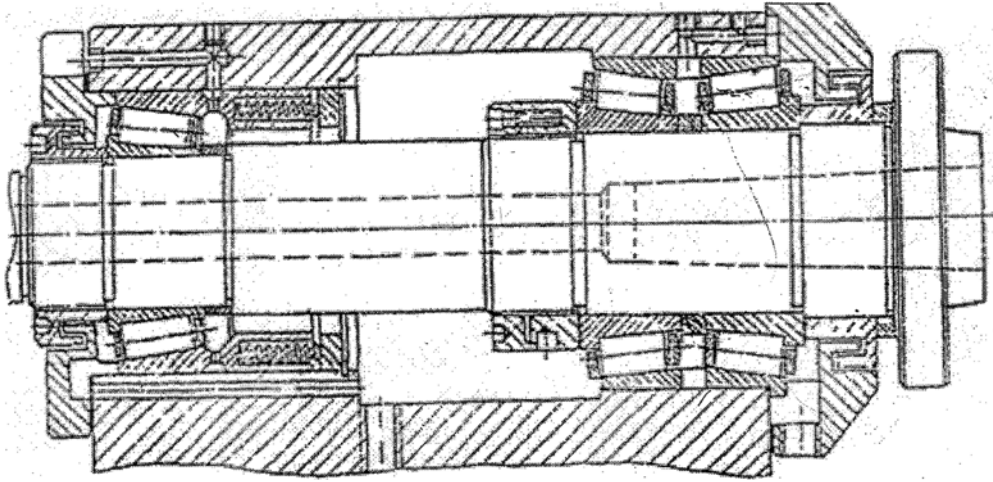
Шпиндельный узел станка с ЧПУ на роликоподшипнике с упорным бортом типа 697000 в передней опоре и однорядном роликоподшипнике типа 17000 с предварительным натягом пружинами в задней опоре
